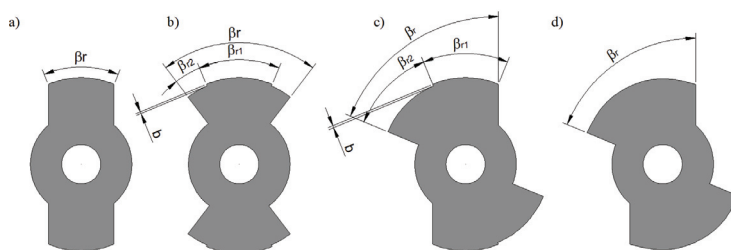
Zaprojektowane konstrukcje stojanów: a) maszyna dwupasmowa, b) trójpasmowa
